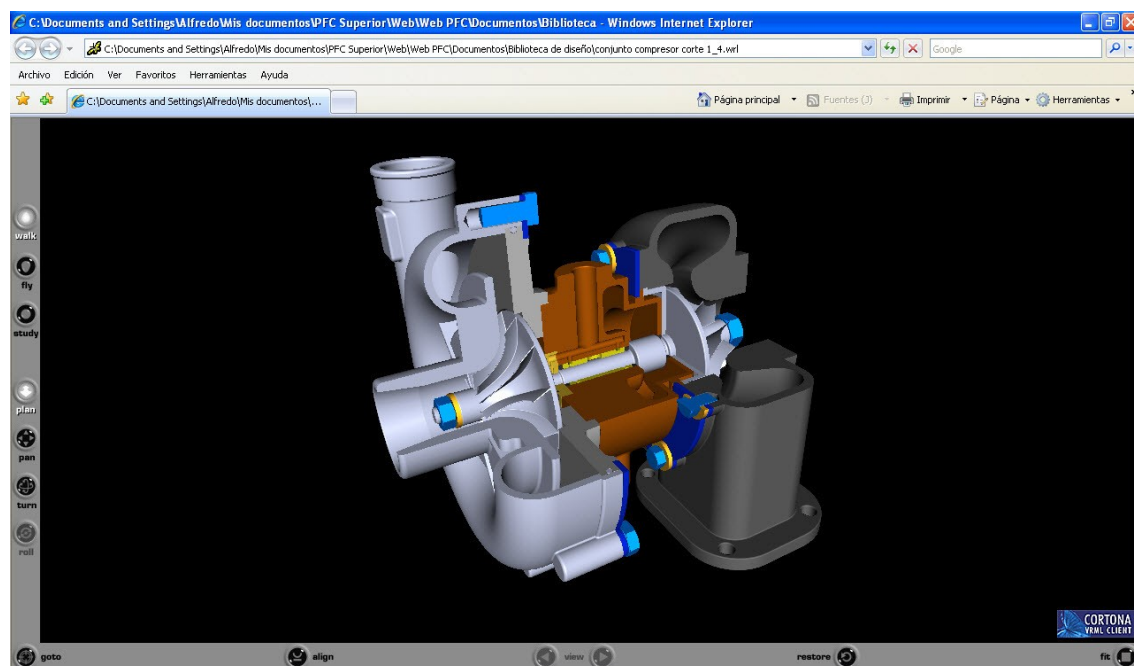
Imagen del Turbocompresor 3D con corte 1/4 en VRML
